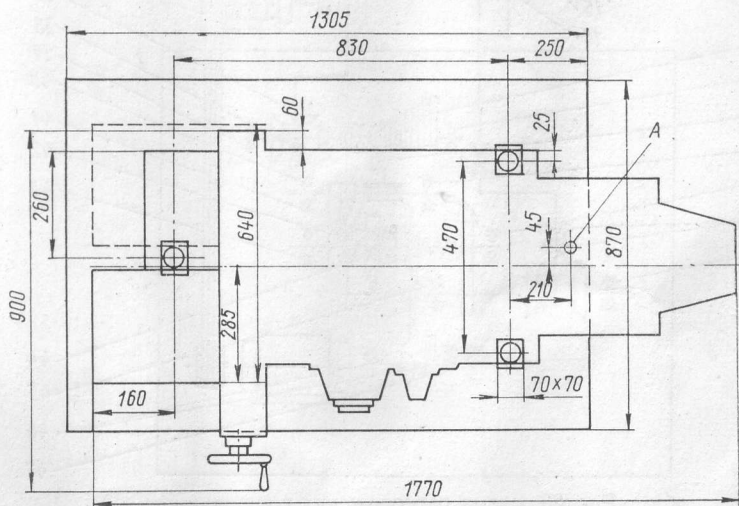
Габаритные размеры и план фундамента станка 7A33:
